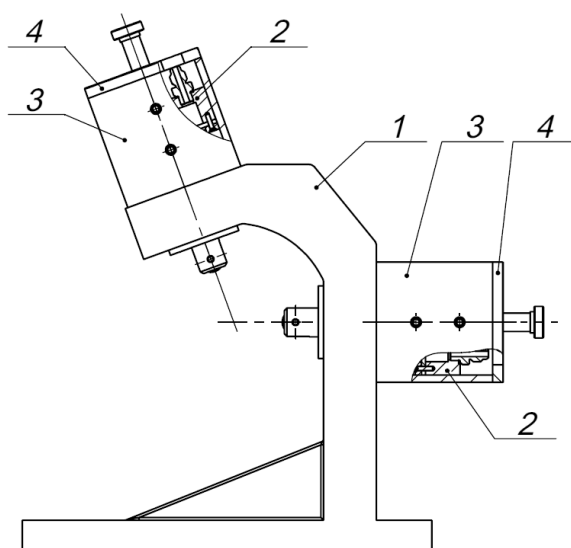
Виброгаситель вязкого трения: 1) стойка; 2) гидроцилиндр; 3) стакан; 4) крышка
